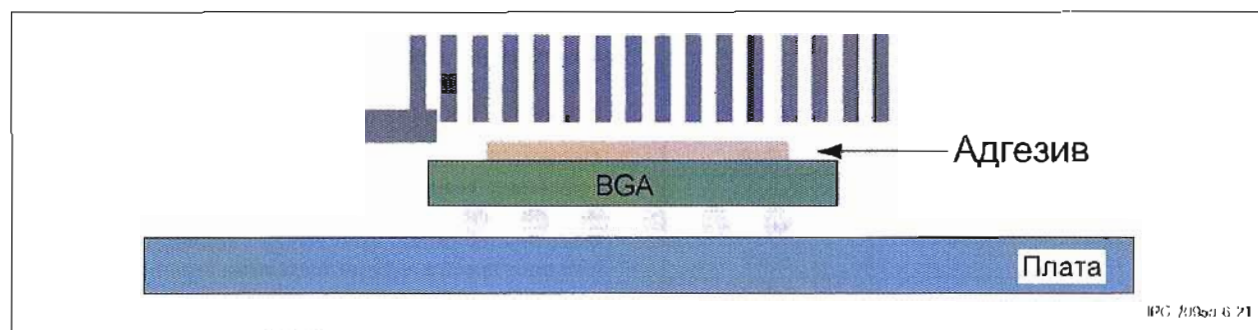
Радиатор, установленный на корпус BGA при помощи адгезива
